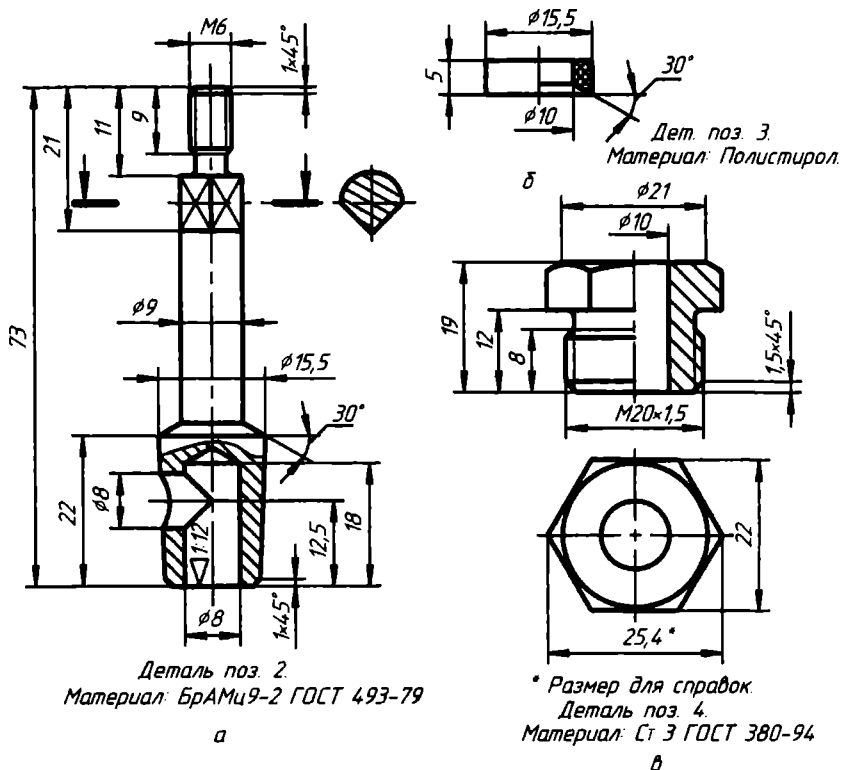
Чертежи: а — пробки; б — кольца; в — втулки
